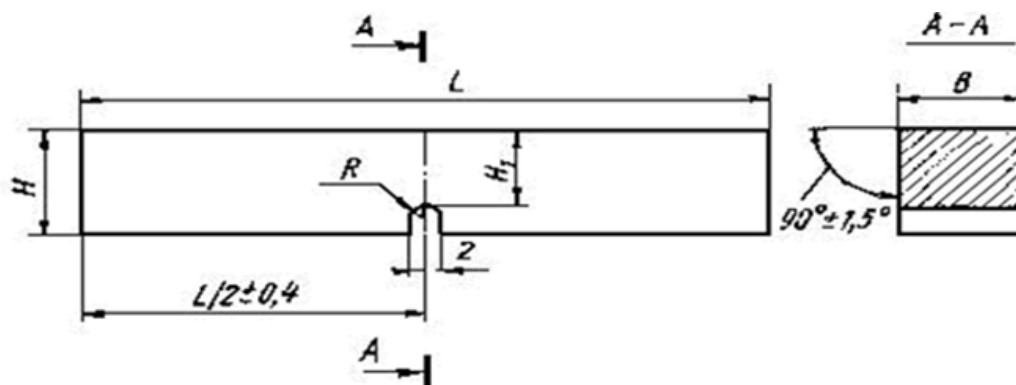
Образец с U-образным надрезом для испытаний на ударный изгиб
